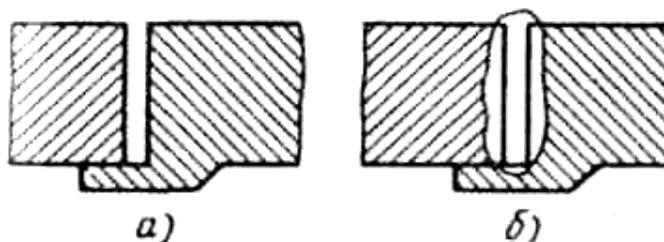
Замковое соединение: а – форма подготовленных кромок; б – форма сварного соединения
